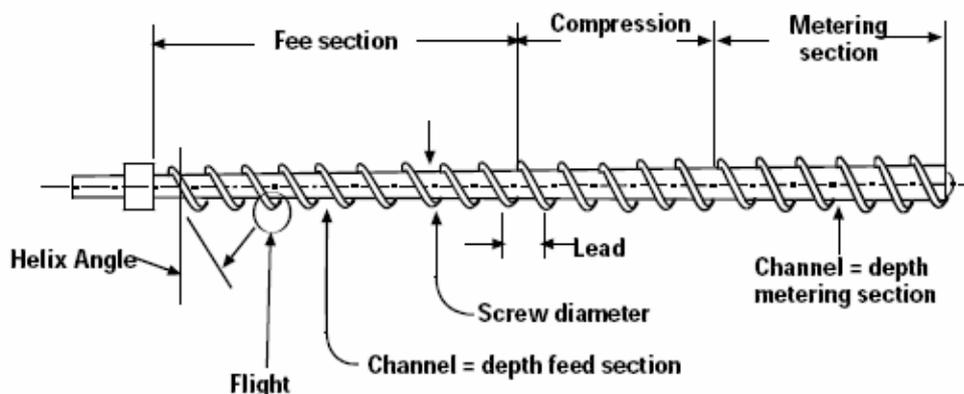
Tornillo extrusor, máquina monohusillo
